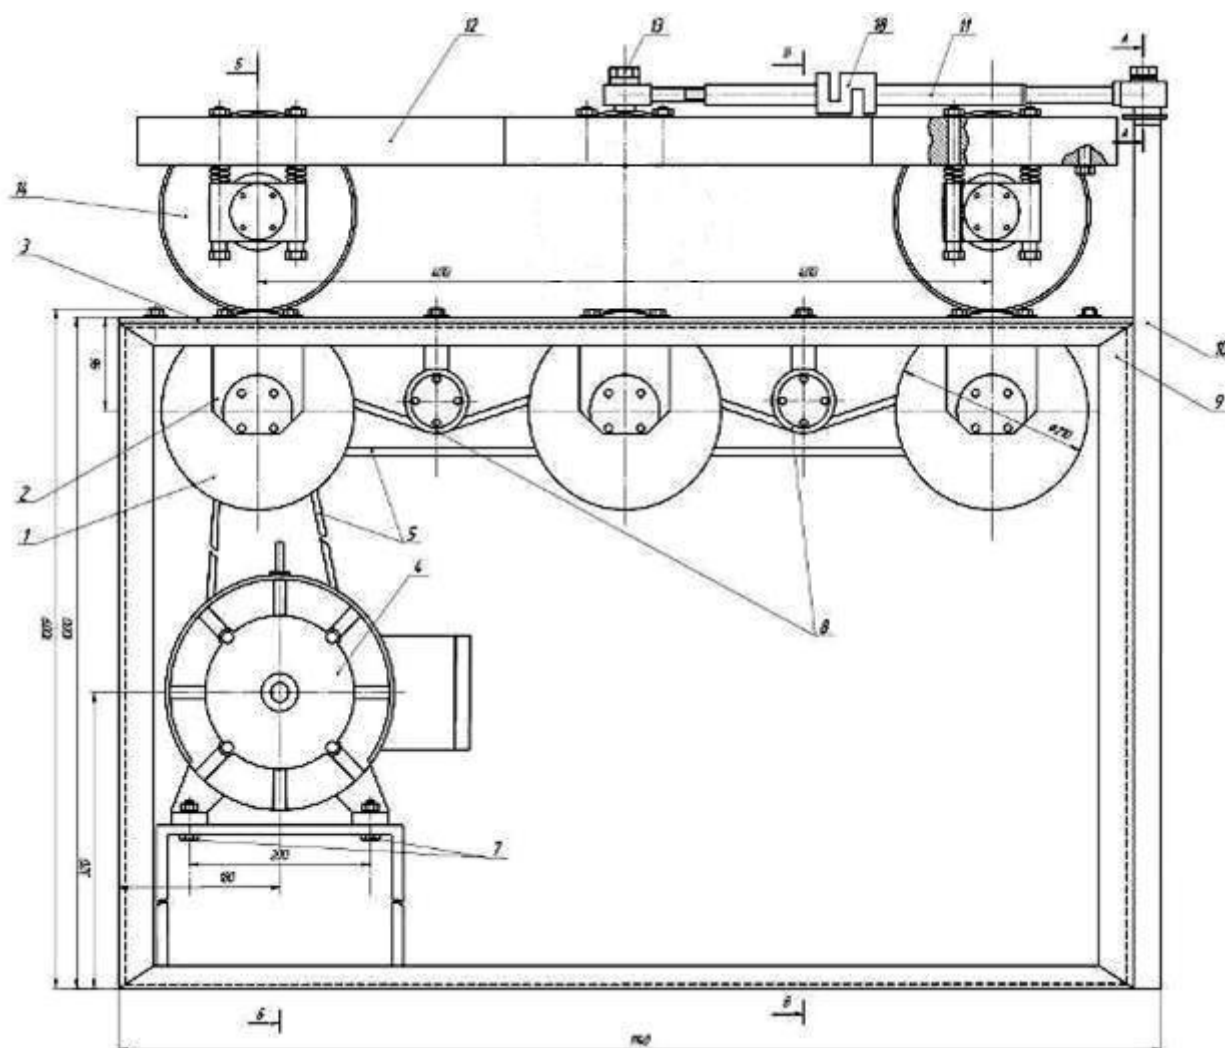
Схема стендової установки (фронтальний вигляд)
